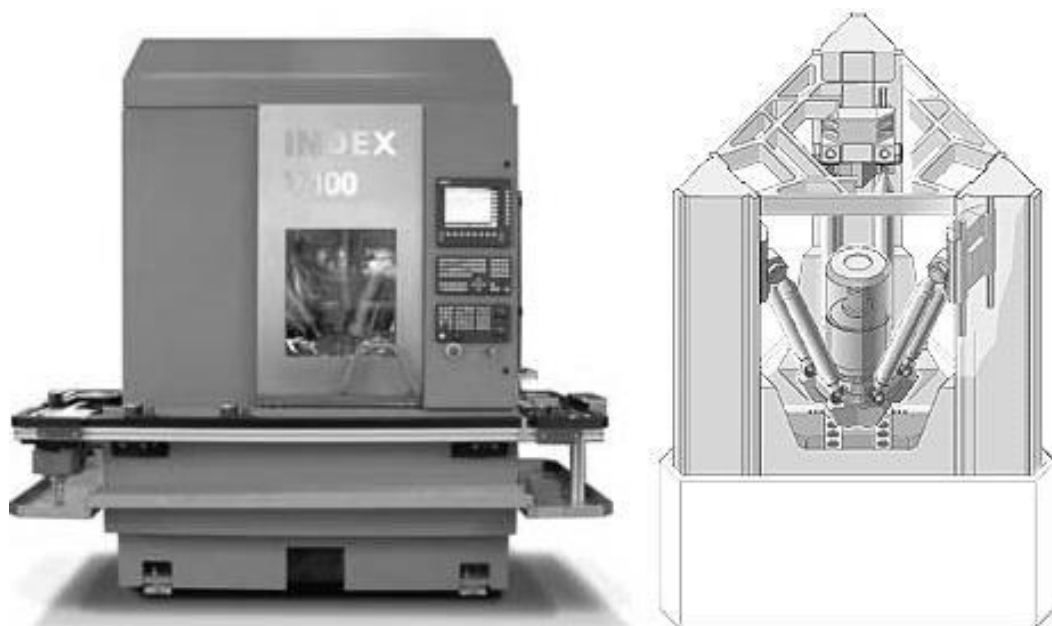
Широкоуніверсальний обробний центр VerticalLine V100 фірми INDEX-Werke
